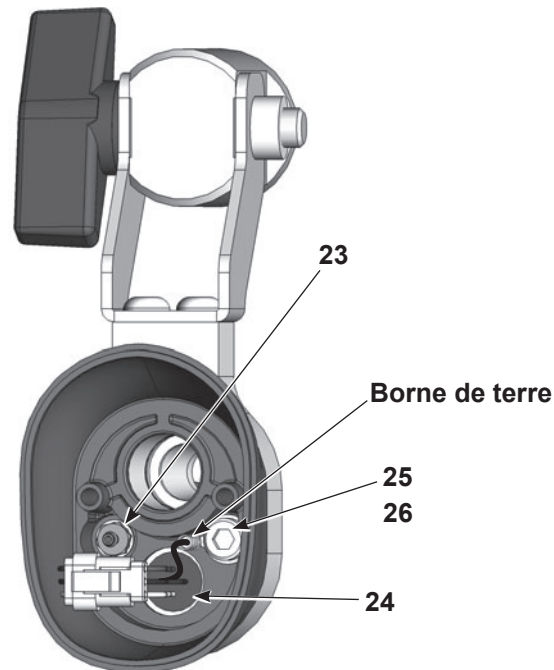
Démontage du pistolet – Remplacement de la prise du câble et du raccord cannelé
